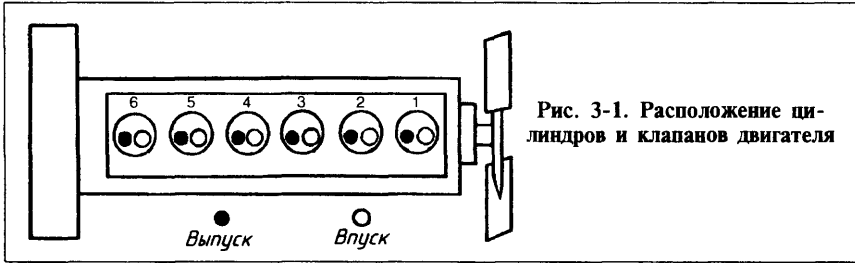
Расположение цилиндров и клапанов двигателя
